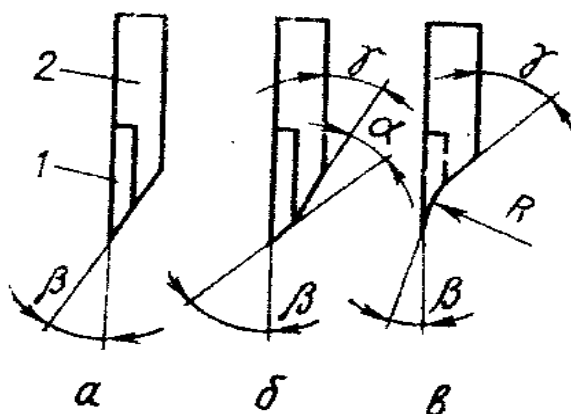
Конструкция ножа бумагорезательной машины и способы его заточки: 1 – режущая часть ножа из легированной стали; 2 – балка ножа, изготовленная из обычной конструкционной стали; а – обычная фаска; б – двойная фаска; в – радиусная заточка, выполненная на шлифовальном станке (радиусом R); α, β, γ – углы ножа
